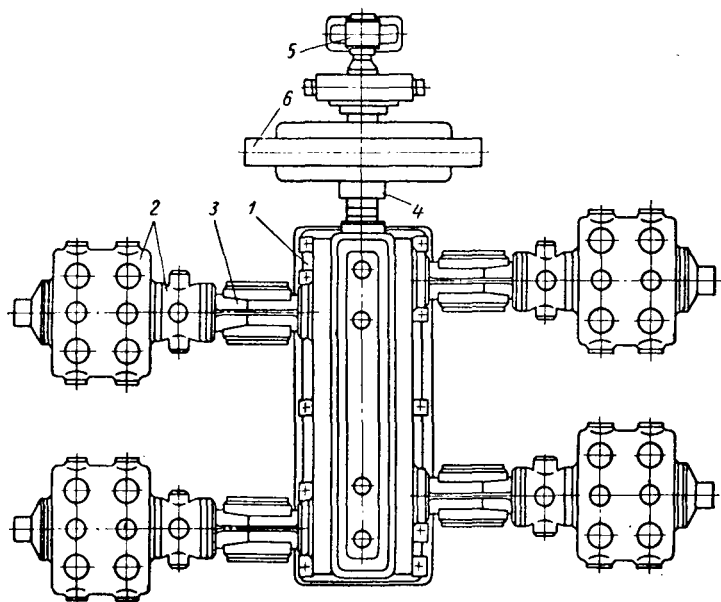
Горизонтальный оппозитный четырехрядный многоступенчатый компрессор:
